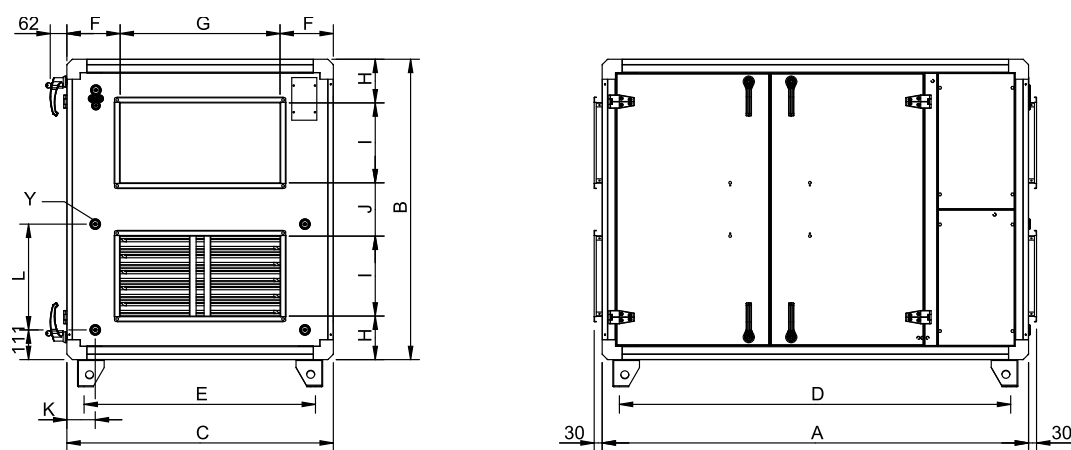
Dimensions (mm) SR04, SR06 (Version droite)
